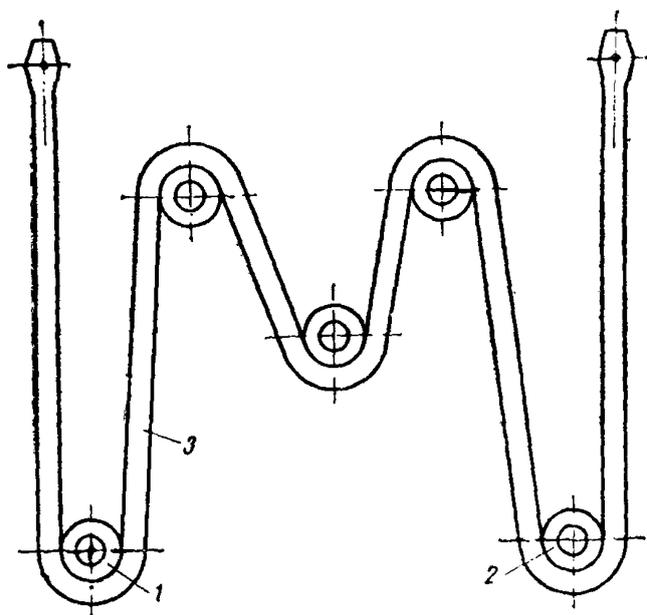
Запасовка шарнирно-пластинчатой цепи
